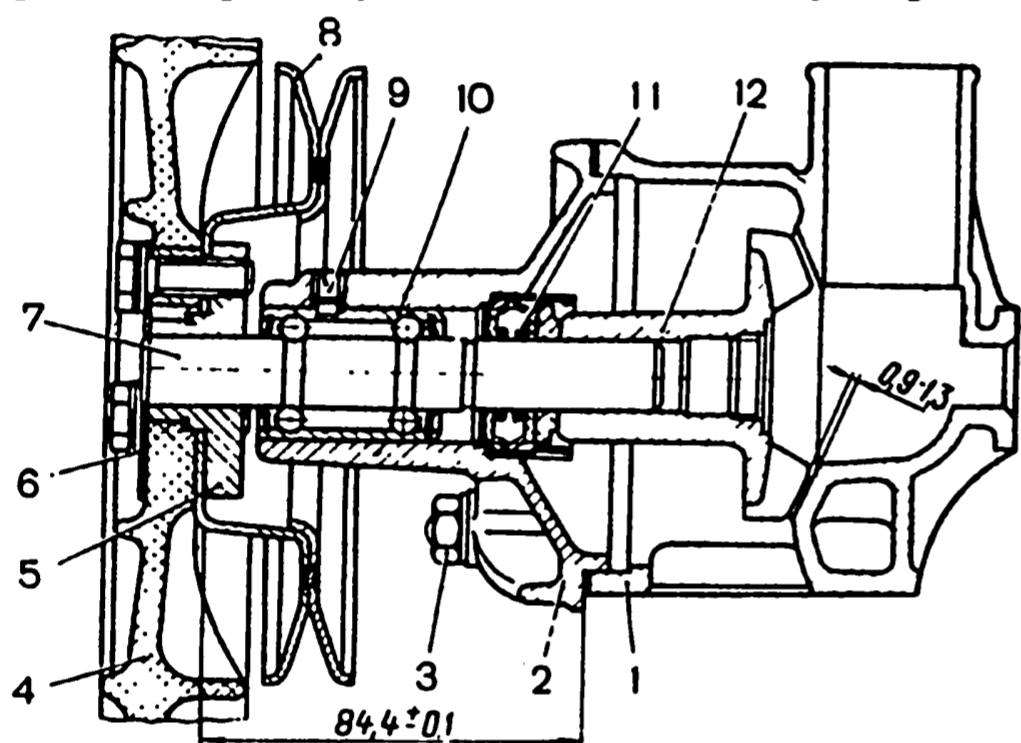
Продольный разрез насоса охлаждающей жидкости: 1 - корпус; 2 - крышка; 3 - гайка крепления крышки насоса; 4 - вентилятор; 5 - ступица шкива; 6 - накладка; 7 - валик; 8 - шкив; 9 - стопорный винт подшипника; 10 - подшипник; 11 - сальник; 12 - крыльчатка
